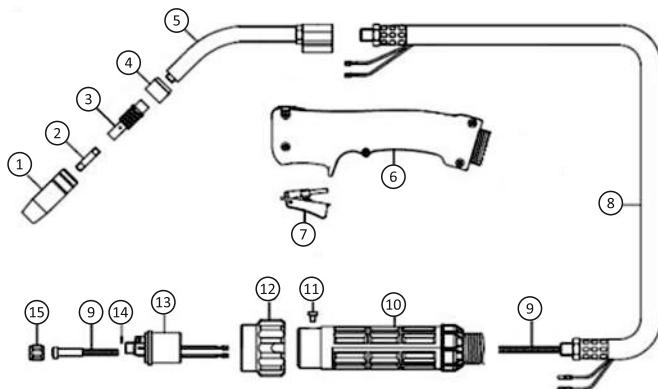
Схема горелки для MIG/MAG сварки
